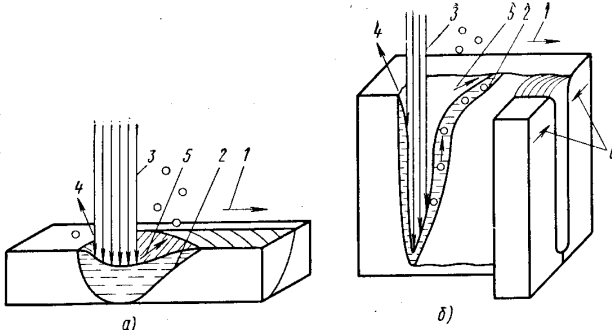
Схема электронно-лучевой сварки металлов малой (а) и большой (б) толщины:
